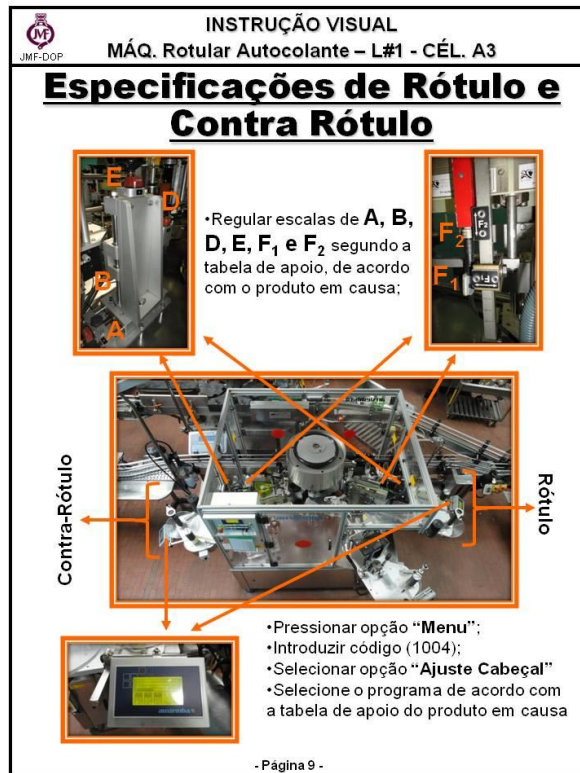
Instrução Visual Rotuladora Autocolante (Parte 6)
